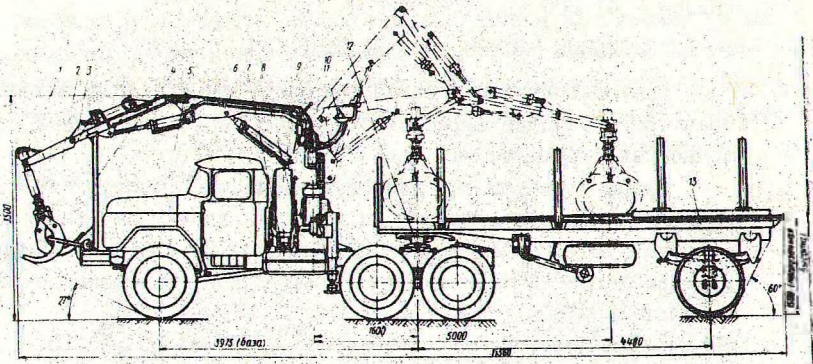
Самозагружающийся автопоезд ЛТТ-95М с гидроманипулятором: 1-гидропривод поворота грейферного захвата; 2-грейферный захват; 3-стрела; 4-опора стрелы; 5-автомобиль-тягач ЗИЛ-131В; 6-гидрокоммуникации; 7-топливный бак; 8-рама гидроманипулятора; 9-гидроцилиндр; 10, 11-сиденье оператора и пульт управления; 12-седло; 13-полуприцеп.
